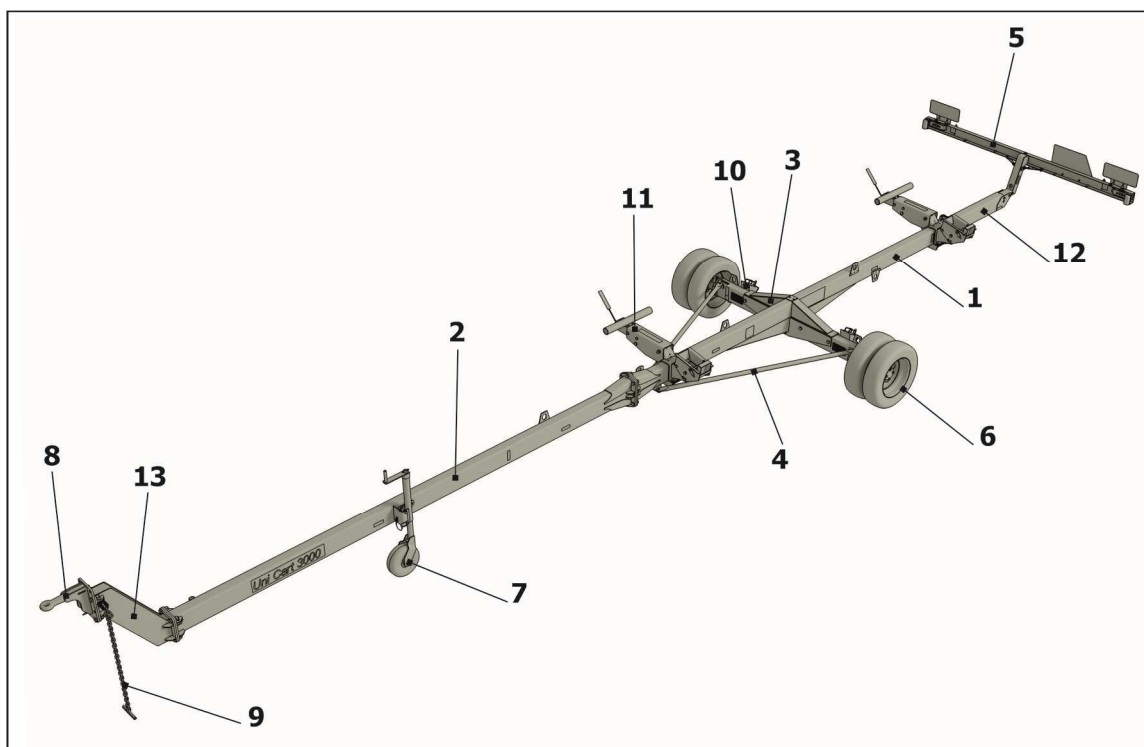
Общий вид приспособления ППА-700-01 "Uni Cart 3000"
